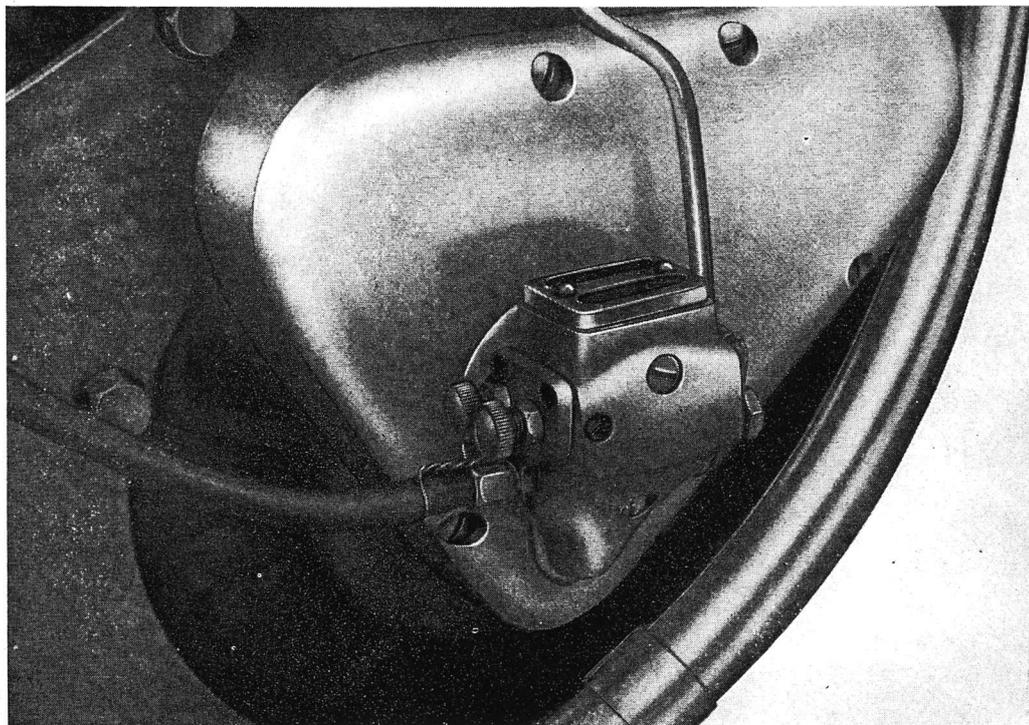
a 2 — Motor připraven ke kontrole časování ventilů
